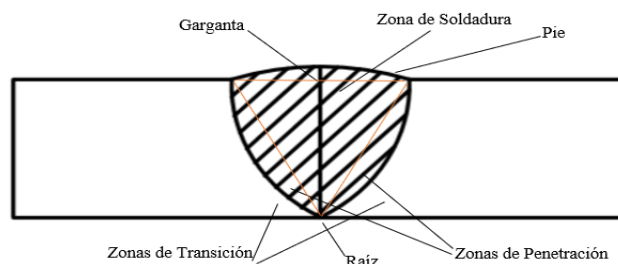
Esquema básico de soldadura por arco
